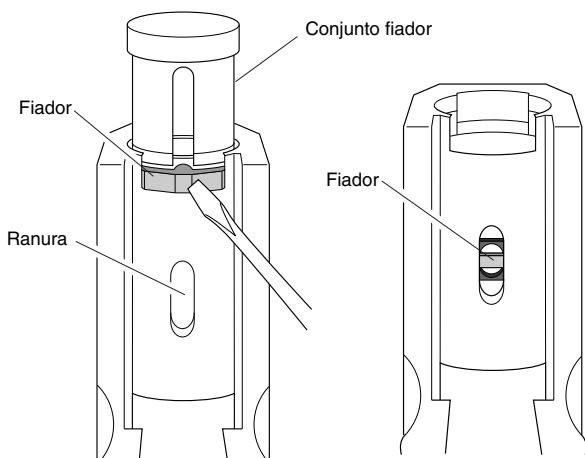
Inserción el conjunto fiador dentro del cilindro visto desde la parte inferior de la herramienta
